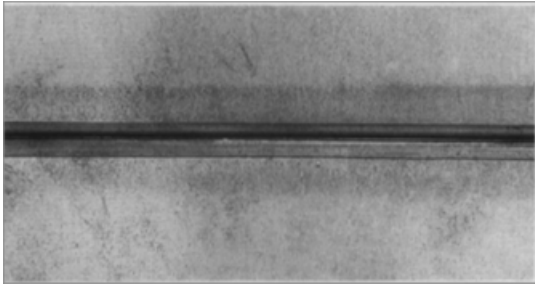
Stauchgrat(-wulst) einer Preßstumpfschweißung an einem Pkw-Felgenreing;
